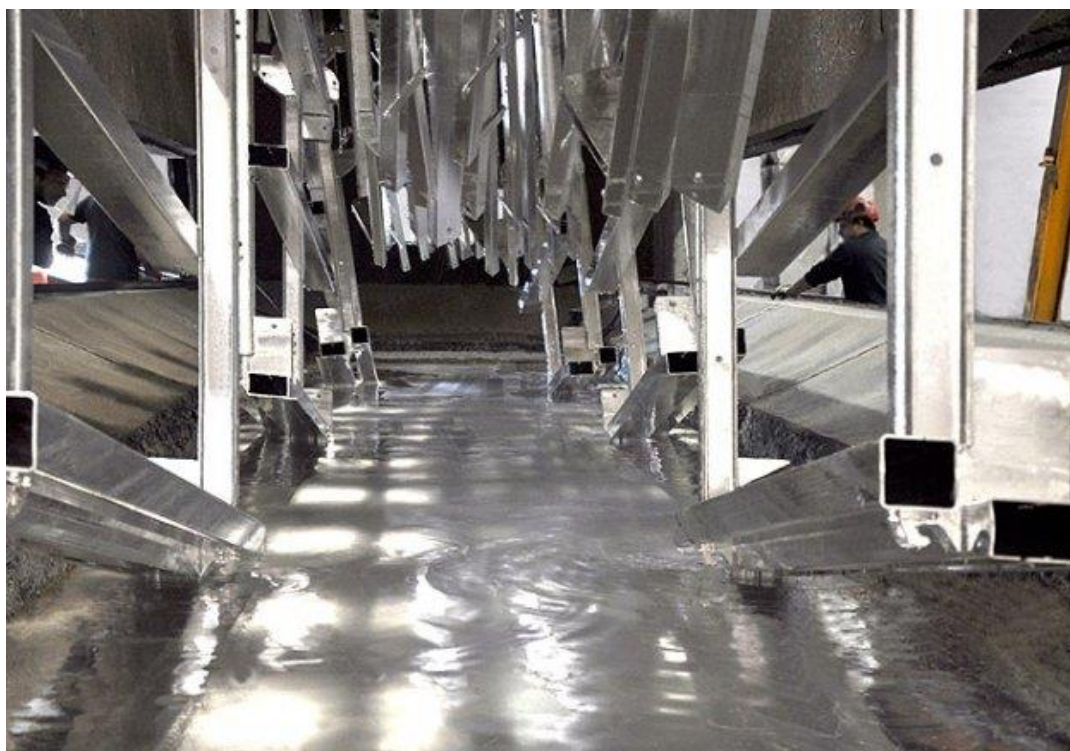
Galvanização de elementos metálicos (<http://www.galvaza.pt/pt/galvanizacao/>)
